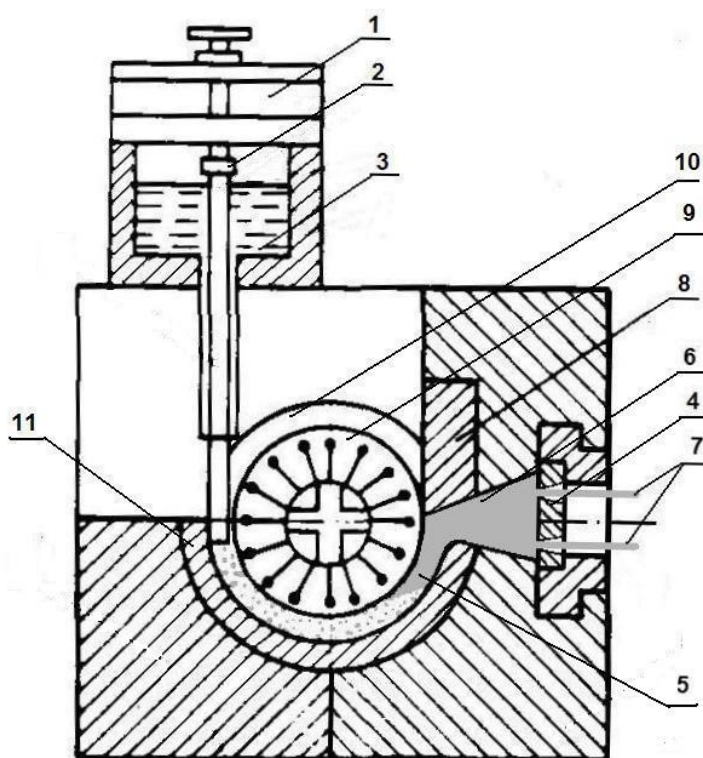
Схема процесса непрерывного прессования Conform-Castex полых профилей из жидкого металла:
